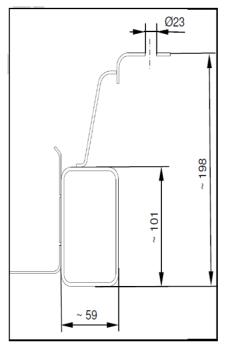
Sezione T-T (Amarok SC/DC)
